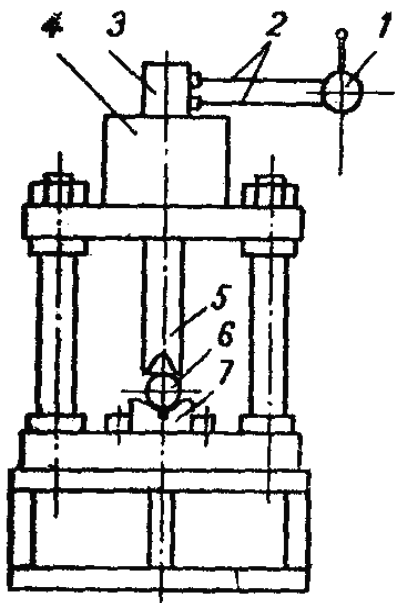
Схема пневматического пресса для правки и рихтовки прутков.
